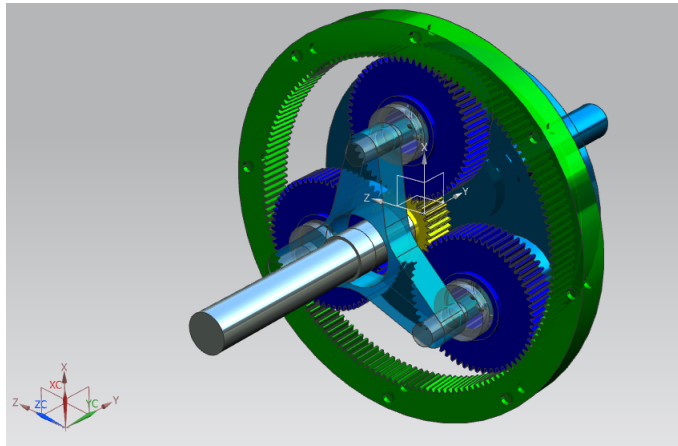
SEP con el eje del engrane solar. La parte de la corona será fabricada con acero inoxidable AISI 303 por ser de fácil mecanizado y resistencia a la corrosión.
